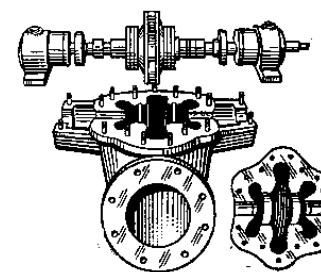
Центробежный одноступенчатый насос типа Д с откинутой крышкой и приподнятым ротором.
